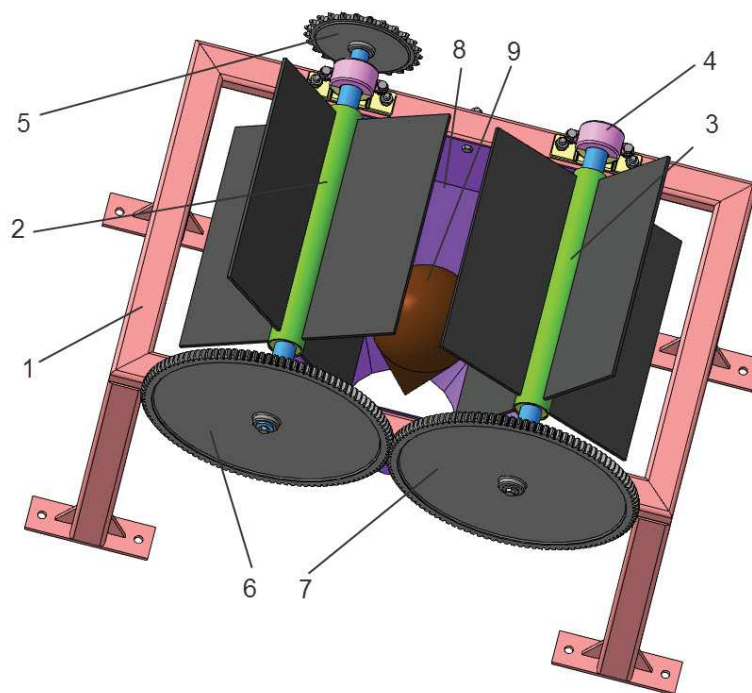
3D-модель ориентирующего устройства: 1 – рама; 2 – ведущий лопастной ротор; 3 – ведомый лопастной ротор; 4 – корпуса подшипников; 5 – звездочка ведущая; 6 – ведущее зубчатое колесо; 7 – ведомое зубчатое колесо; 8 – приемный лоток; 9 – корнеплод
